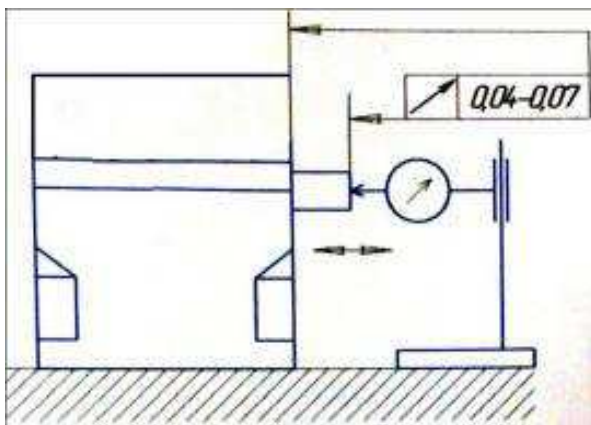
Схема контроля радиального биения исполнительной поверхности выходного вала
